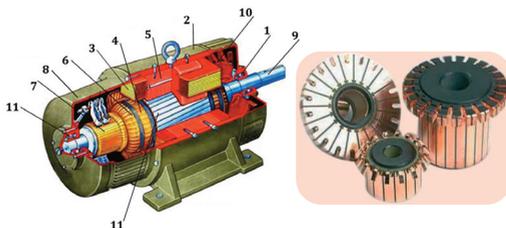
Устройство коллекторного электродвигателя: а – общее устройство; б – медные пластины коллектора
